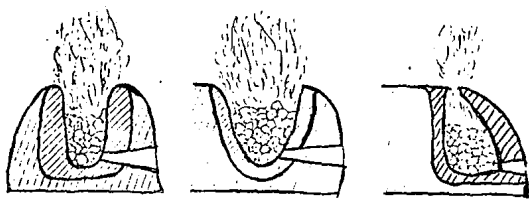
Tipos de hornos primitivos, para fabricar hierro directo del mineral.
